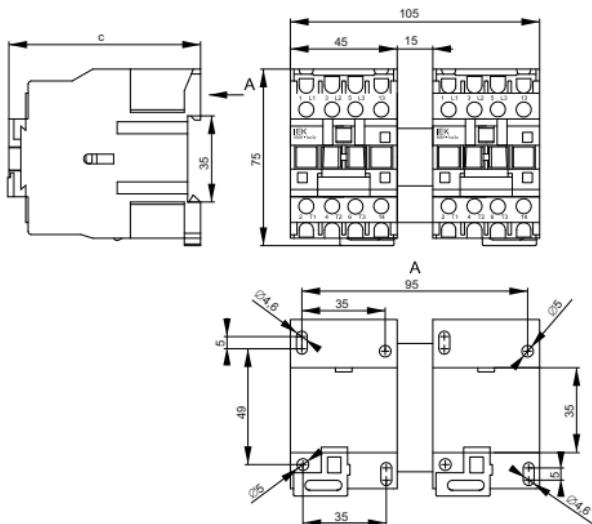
Габаритные и установочные размеры КМИ-10930, КМИ-11230, КМИ-11830 /
